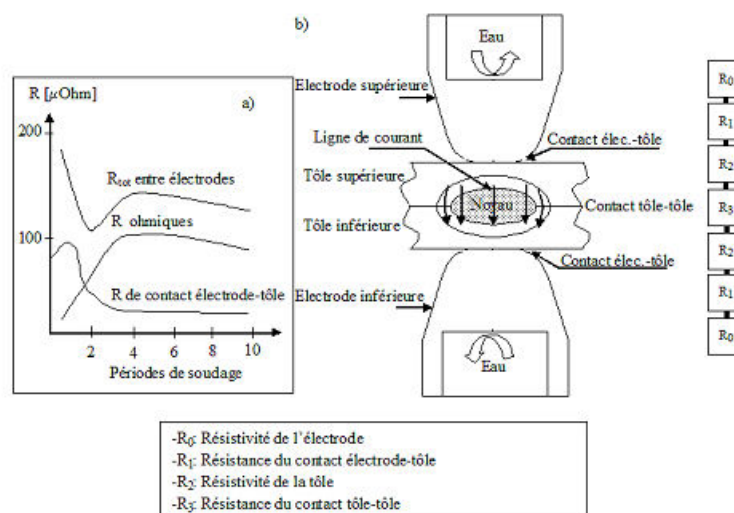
Phénomènes électriques dans le procédé de soudage par points
